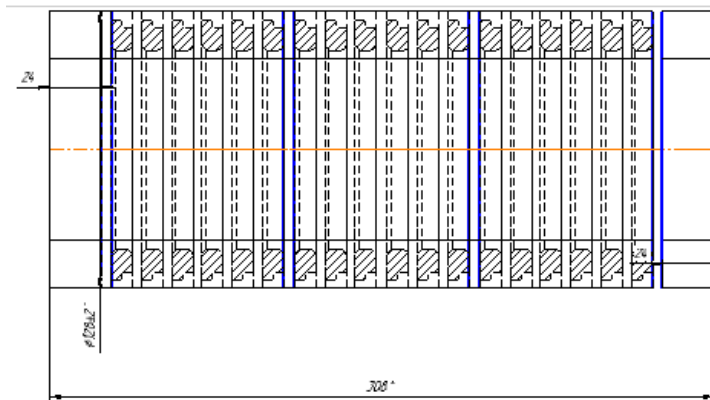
Комплектна заготовка з трьох частин по 6 кілець в кожній
